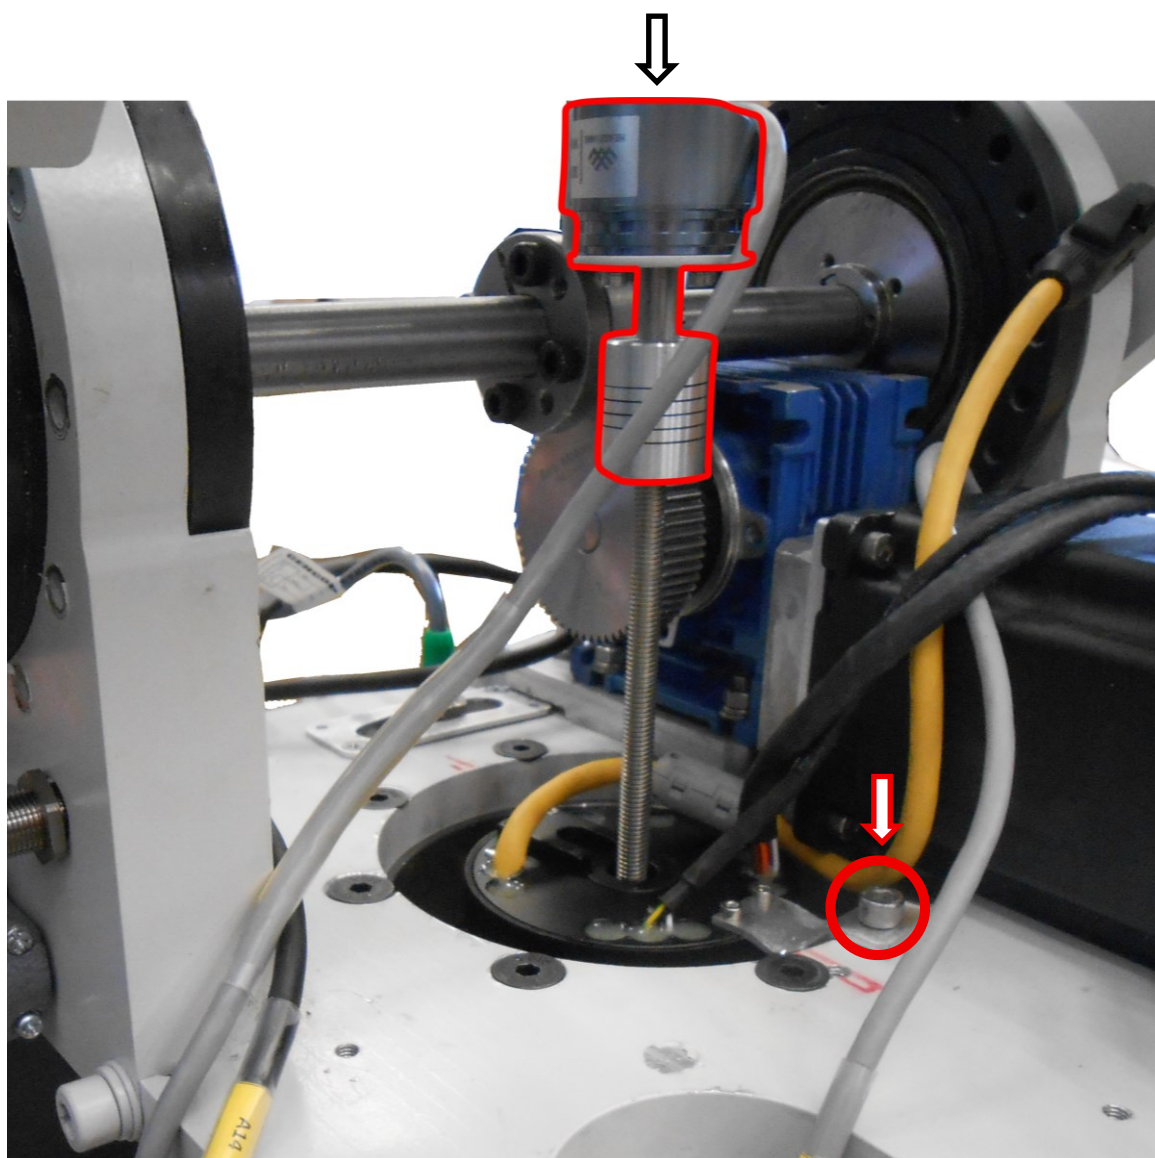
Установка ДУП и крепежа Slip Ring
